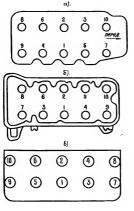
Последовательность затяжки гаек крепления головки блока цилиндров двигателей:
